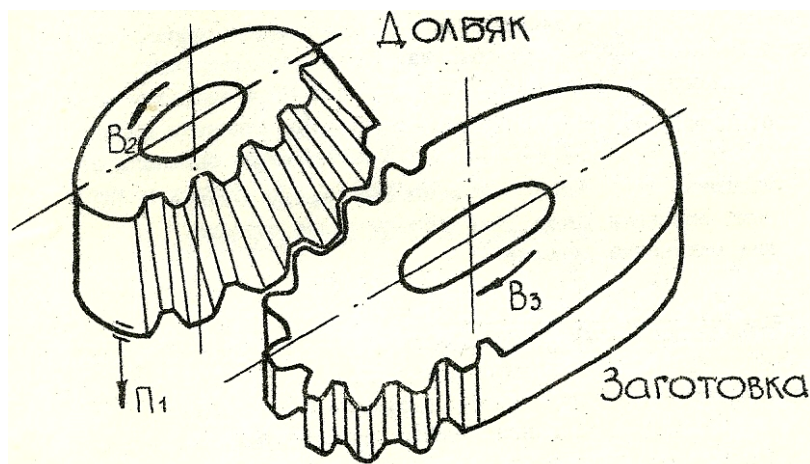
Эскиз зацепления инструмента с заготовкой
